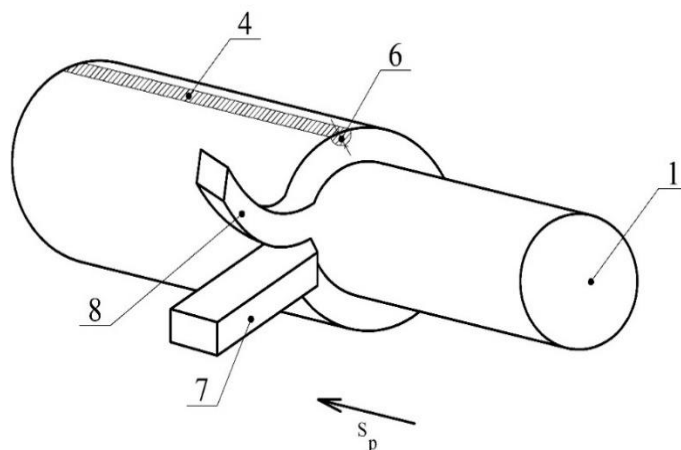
Схема процесса механической обработки заготовки с метастабильной структурой, где: 6 – глубина метастабильной структуры; 7 – режущий инструмент; 8 – стружка
